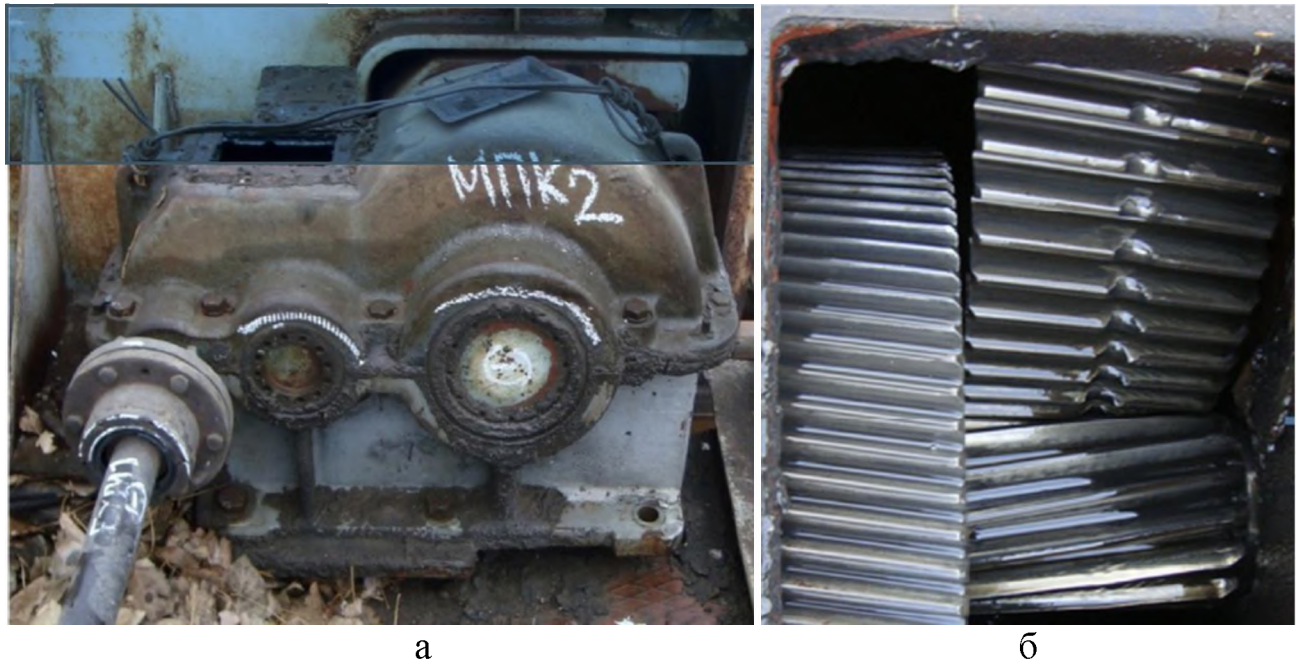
Руйнування зубів зубчастого колеса редуктора механізму переміщення мостового крана 15 т: а – загальний вигляд; б – руйнування зубів
